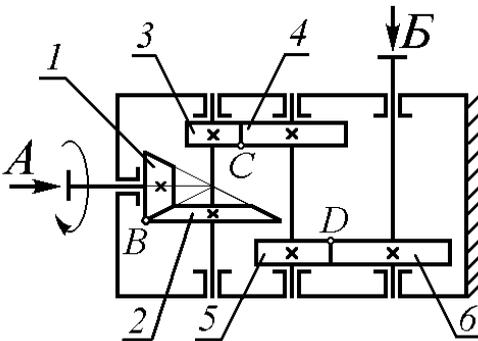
Триступінчастий конічно-циліндричний редуктор
